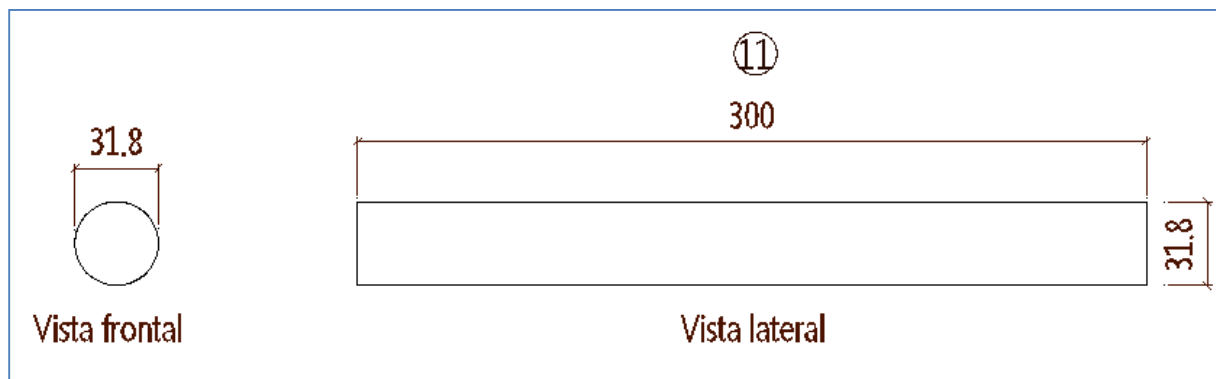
Detalle despiece pieza No.11 modelo 2 tensión.
